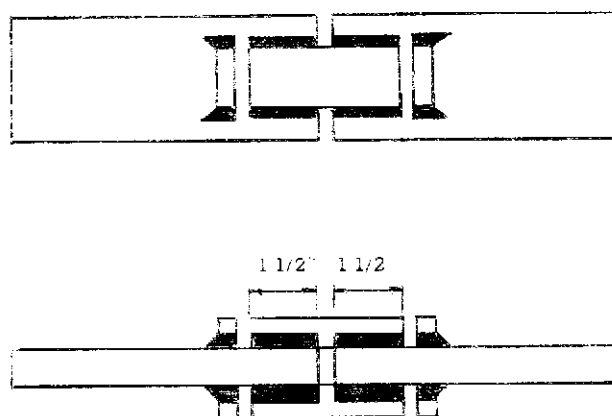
Especimen de filete longitudinal preparado para el ensayo de corte.
